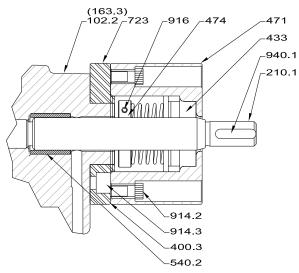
Desenho em Corte bomba FBE c/ selo mecânico
